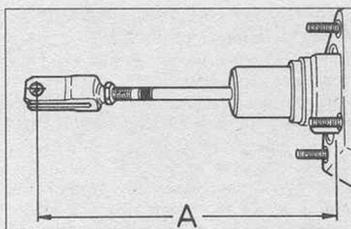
Параметры установки толкателя вакуумного сервопривода (Глава 17)
